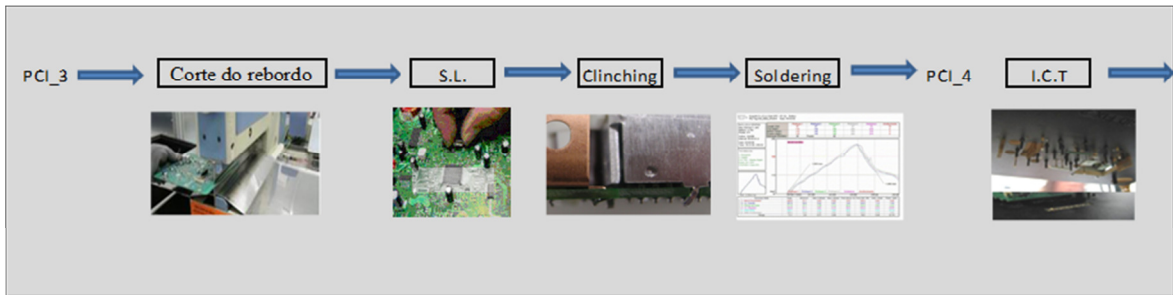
Diagrama do processo inserção manual e soldadura overflow
